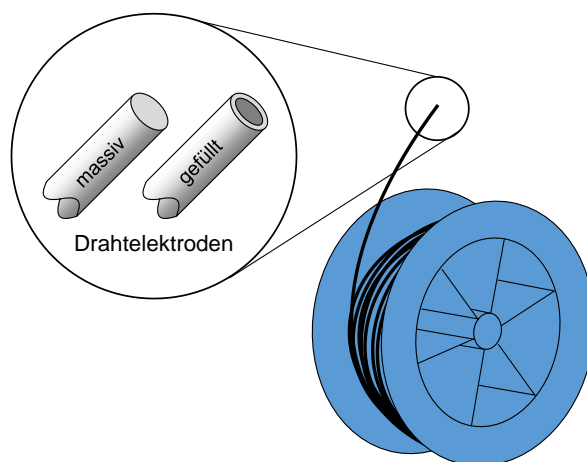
Schweißzusatzwerkstoffe für das Metall-Schutzgasschweißen
